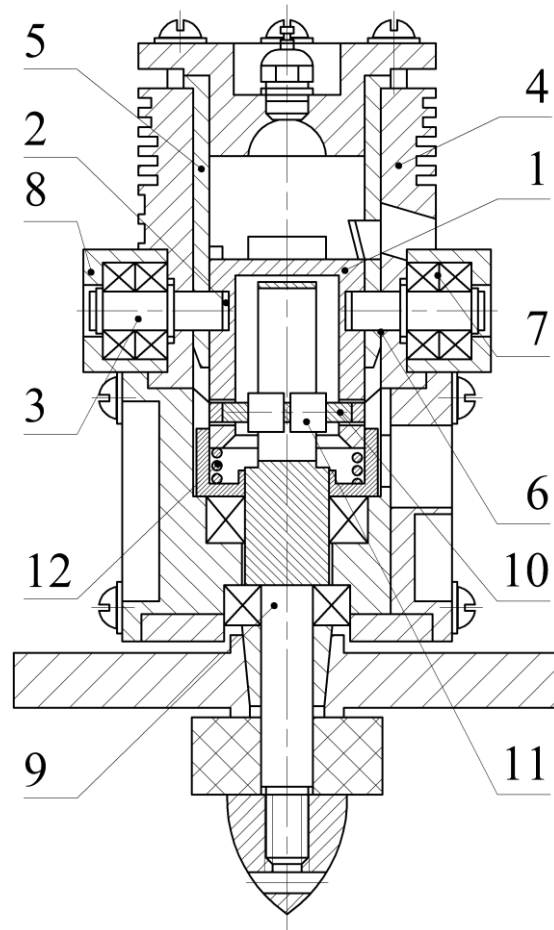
Конструктивная схема бескривошипного двигателя с непосредственным преобразованием возвратно-поступательного движения поршня во вращательное выходного вала: 1 – поршень; 2 – замкнутый криволинейный двухпериодный паз (беговая дорожка) на боковой поверхности поршня; 3 – ролики механизма преобразования движения; 4 – цилиндр; 5 – гильза цилиндра; 6 – отверстия в стенках для роликов; 7 – подшипники; 8 – гнёзда подшипников; 9 – выходной (грузовой) вал; 10 – поршневой палец; 11 – ролики поршневого пальца; 12 – пружина
